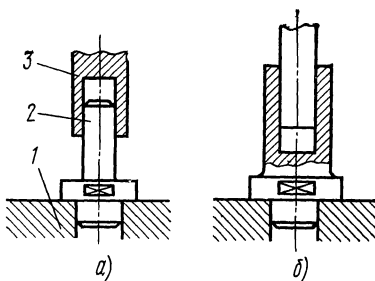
Выверка на соосность стола и инструмента с помощью оправок:
